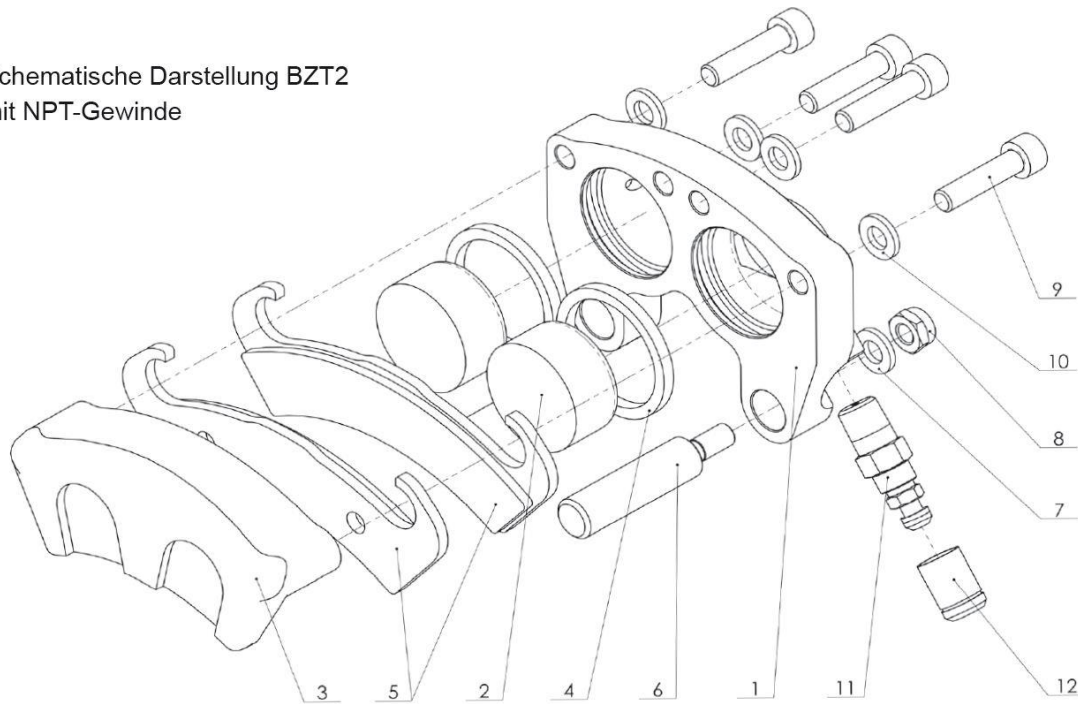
Aufbau Bremszange / *mounted brake calliper
